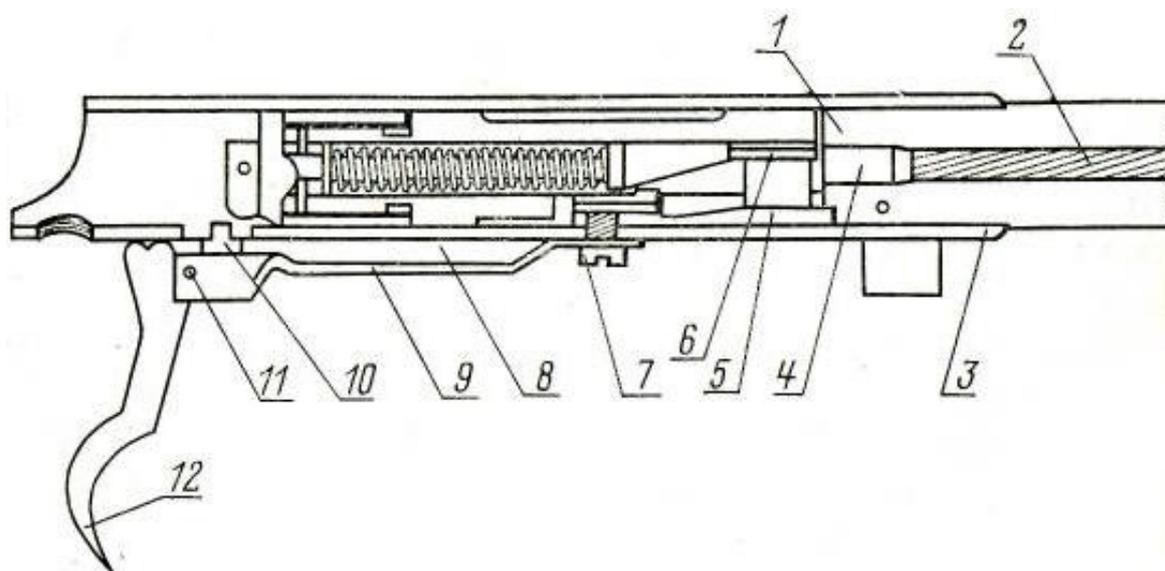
Положение частей винтовки после выстрела: 1 — патронник; 2 — канал ствола; 3 — нижняя часть ствольной коробки; 4 — гильза; 5 — вкладыш; 6 — боек; 7 — винт; 8—12 — спусковой механизм (9 — спусковая пружина; 10 — шептало; 11 — ось; 12 — спусковой крючок).
